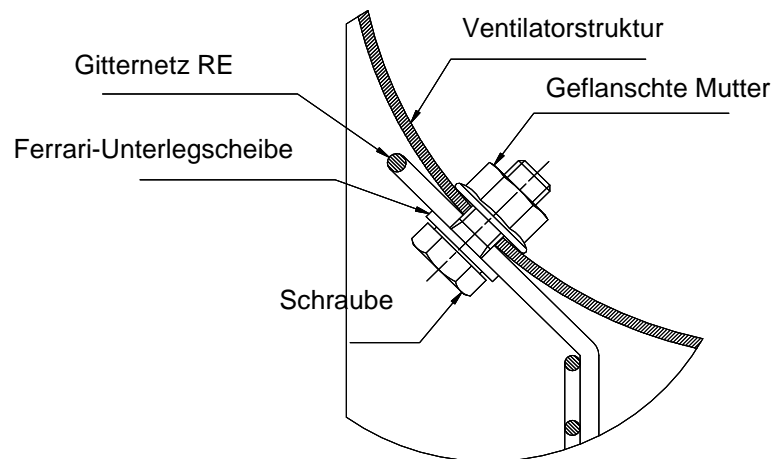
Montageplan der Schutzeinrichtung RE
